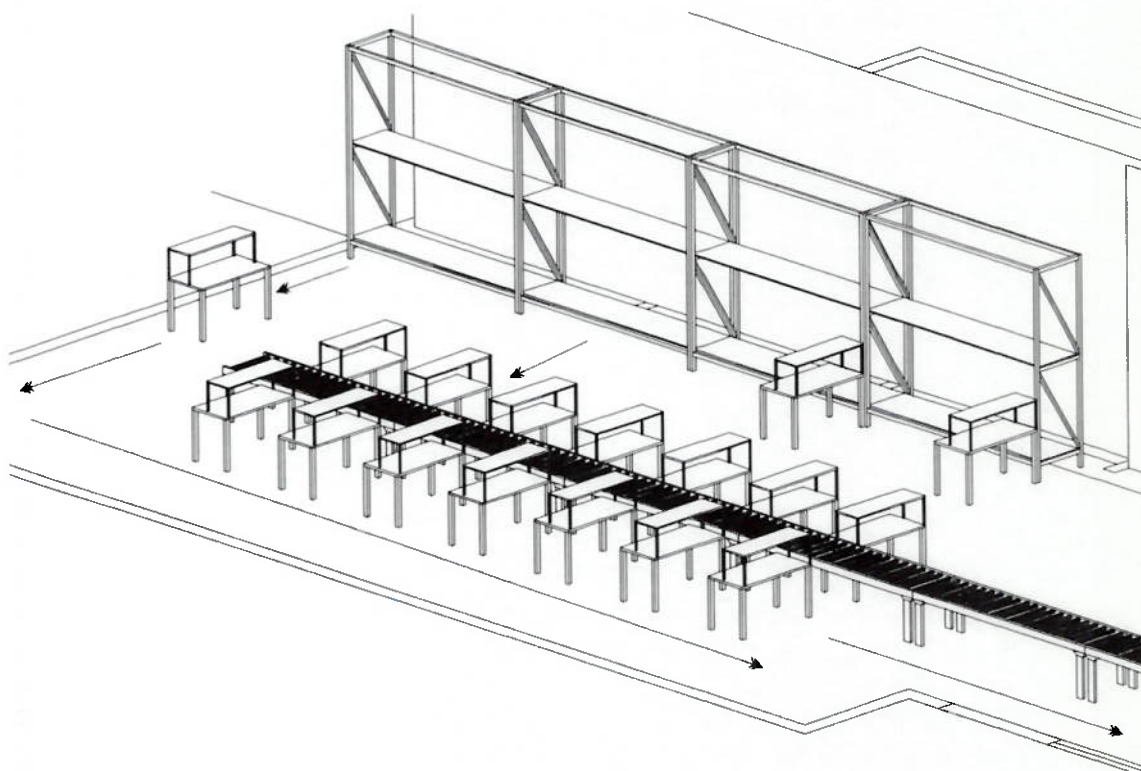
(a): Vista dos postos de inspeção visual, teste e configuração de placa, e gravação de winchester no lay-out antigo. (Elaborada pelo autor)
